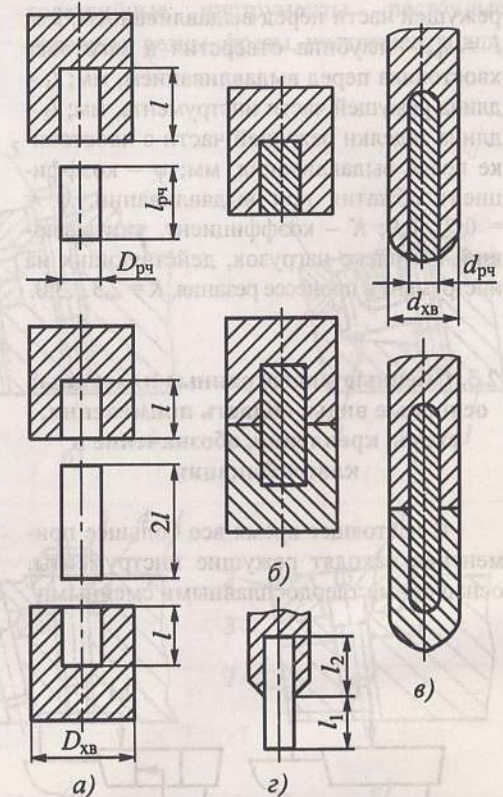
Заготовки для получения биметаллических концевых инструментов:
